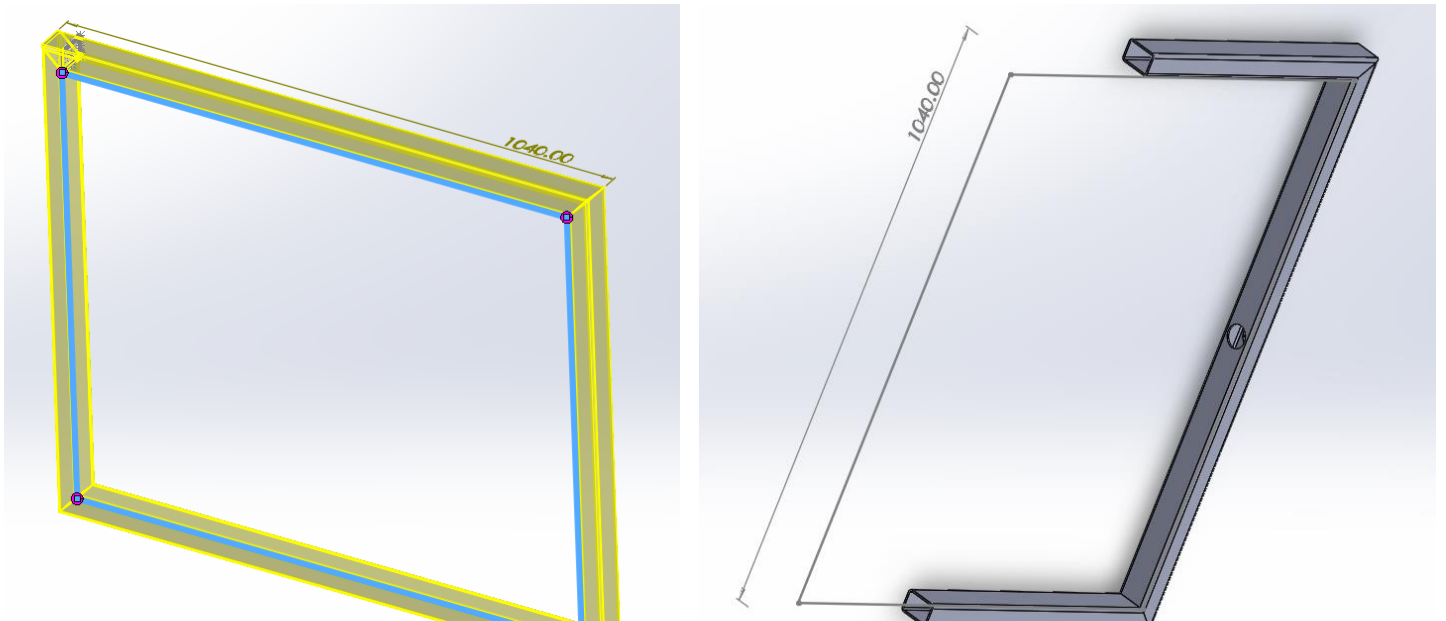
cadre 01 sous forme poutre et la vue en coupe
